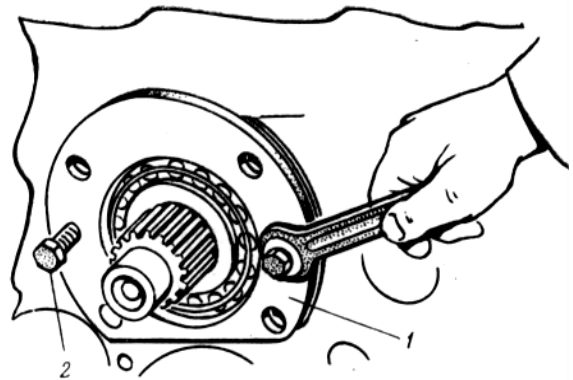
Випресування стакана підшипника вторинного вала: 1-стакан підшипника; 2- технологічний болт
